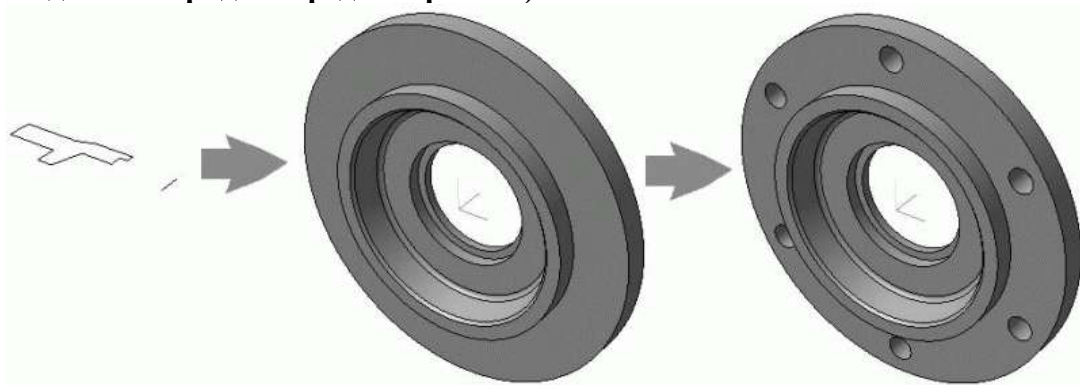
Построение 3D-модели сквозной крышки подшипника
